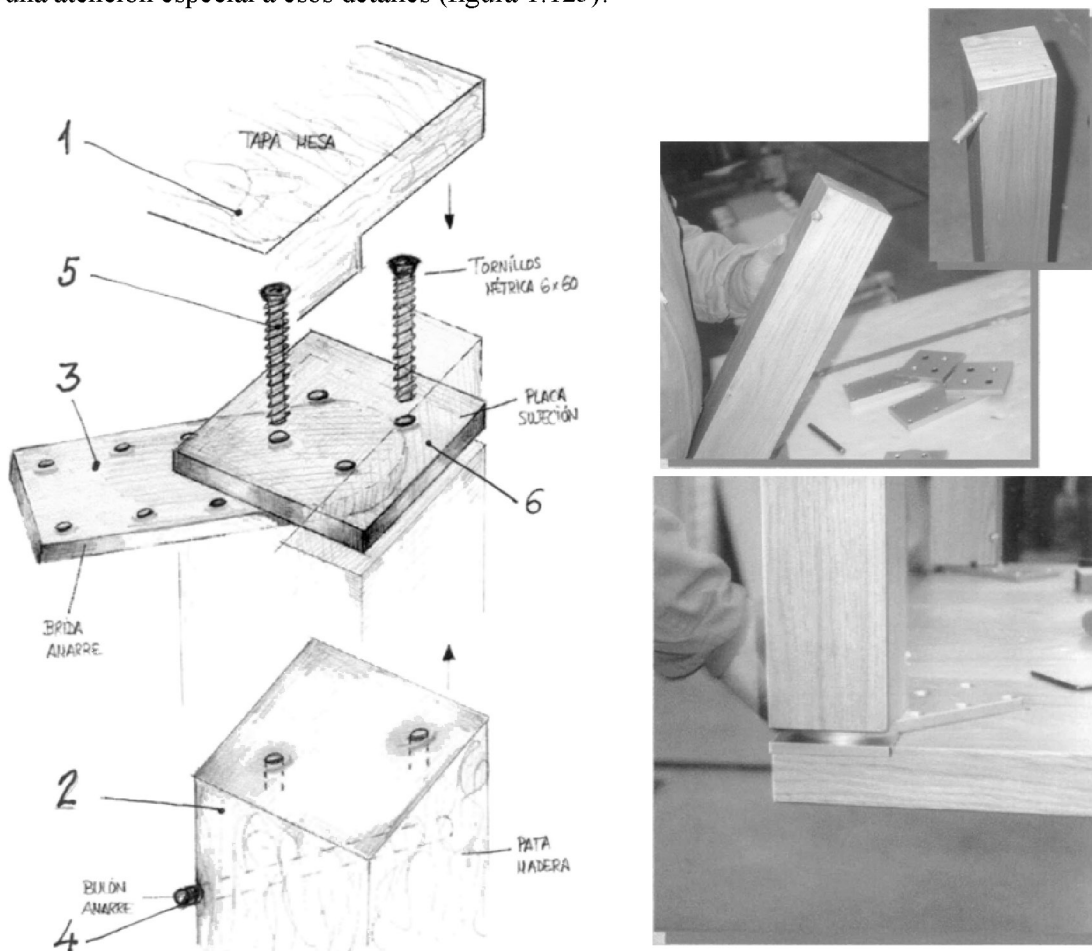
Detalle del plano de diseño de un herraje metálico para un mueble de madera (izquierda) y fotografía del montaje final (derecha). (Fuente: E. López)
